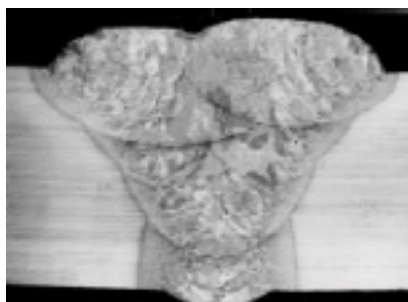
Ti6Al4V (20mm) soldado por MIG. [40]
